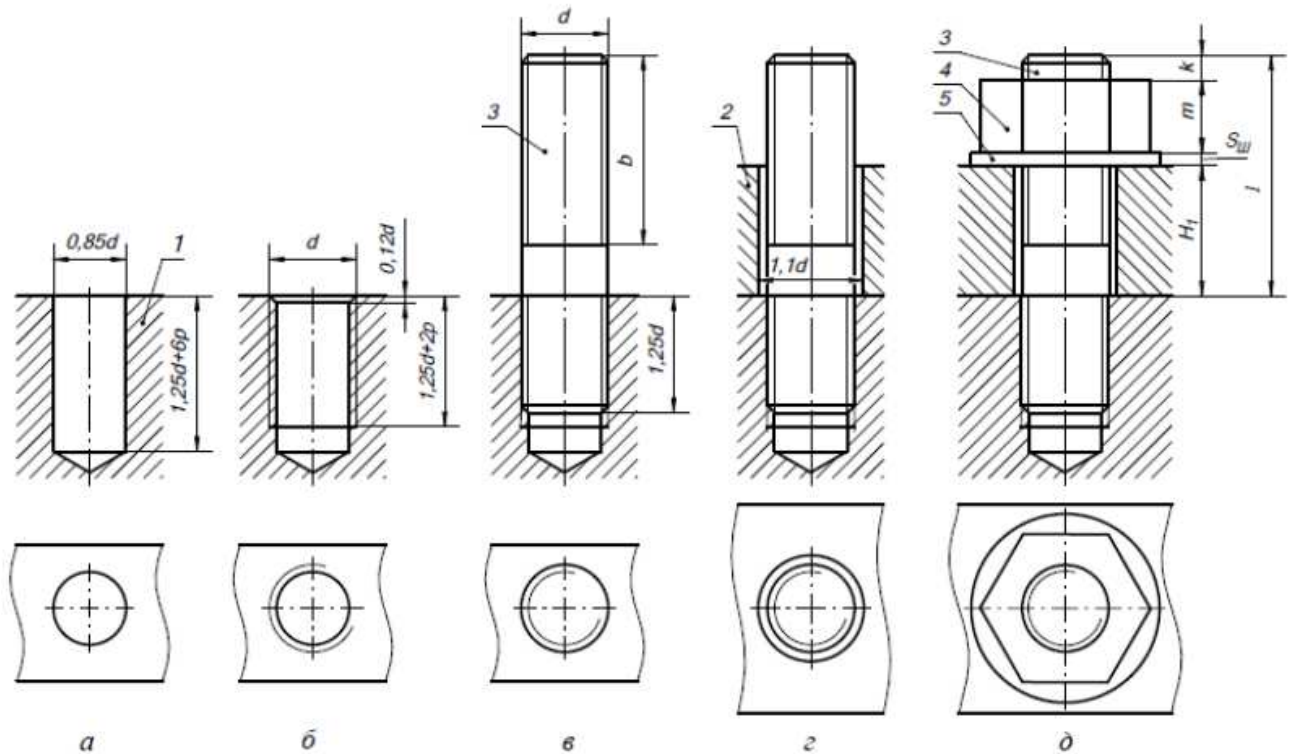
Конструктивне зображення шпилькового з'єднання
